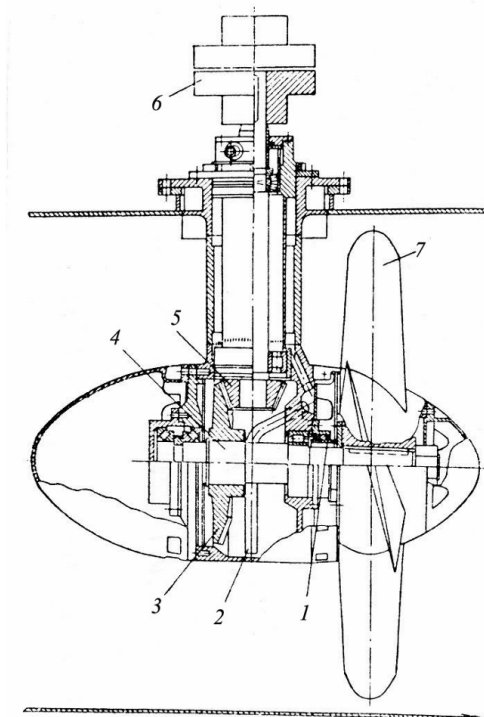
Конструкція одnogвинтового ПП з використанням зубчастого конічного редуктора: 1 – ущільнення гребного валу; 2 – трубка для відкачування мастила; 3 – конічне зубчасте колесо; 4 – гребний вал; 5 – конічна шестерня; 6 – сполучна муфта; 7 – гребний гвинт
